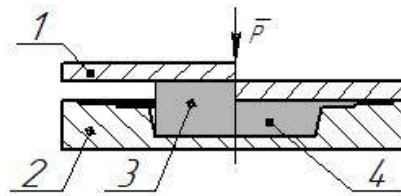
Схема гарячого деформування: 1- бойок; 2 - матриця; 3 - заготовка; 4 – поковка
